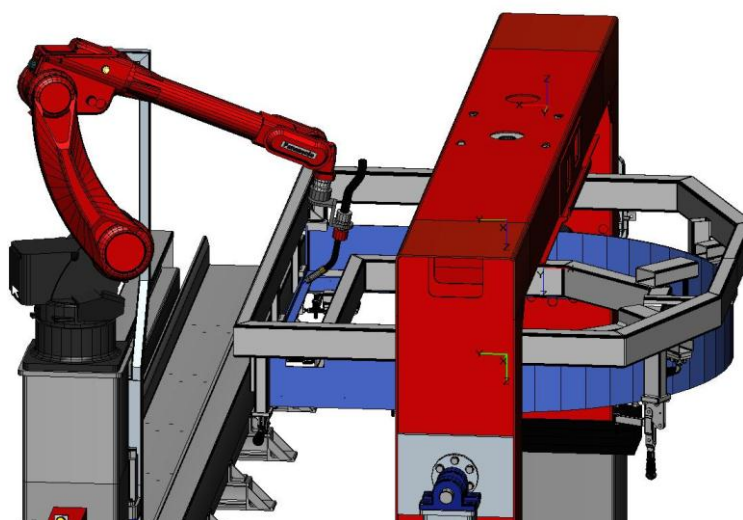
Ukázka pohybu robota při svařování z horní strany
